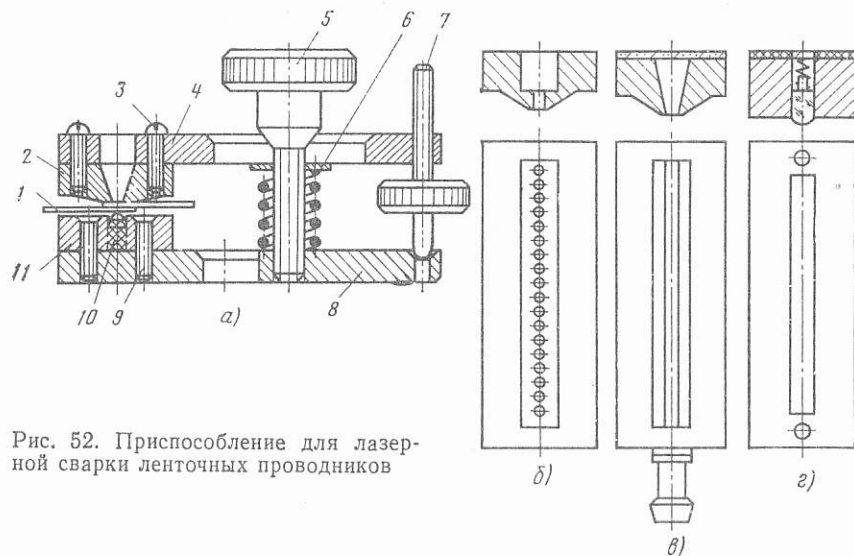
Приспособление для лазерной сварки ленточных проводников
